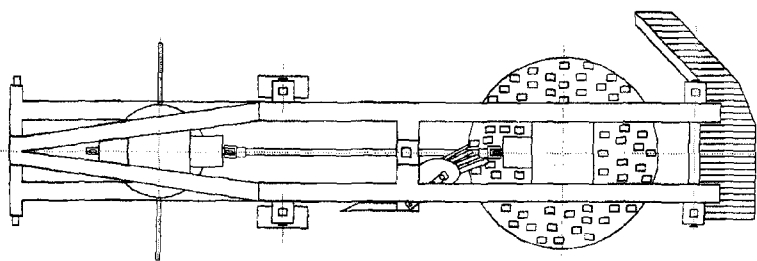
Измельчающе-подкапывающий агрегат, вид сверху
